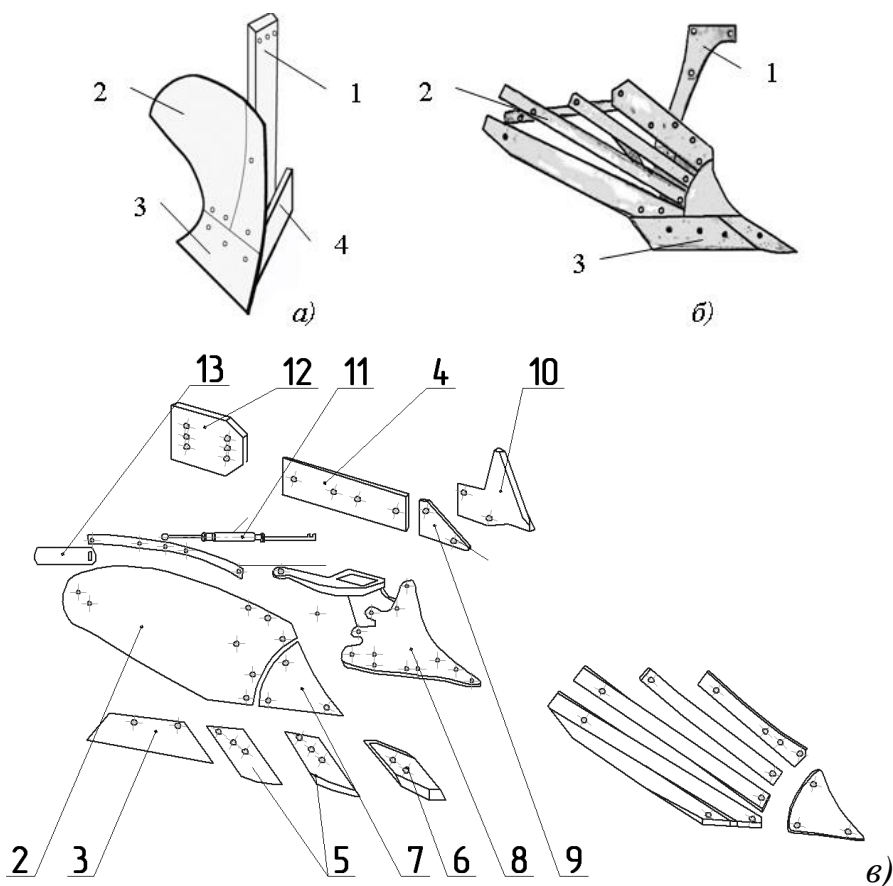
Корпуса для отвальной вспашки а) корпус обычный; б) корпус с пластинчатым «перьевым» отвалом; в) основные узлы корпусов плугов
